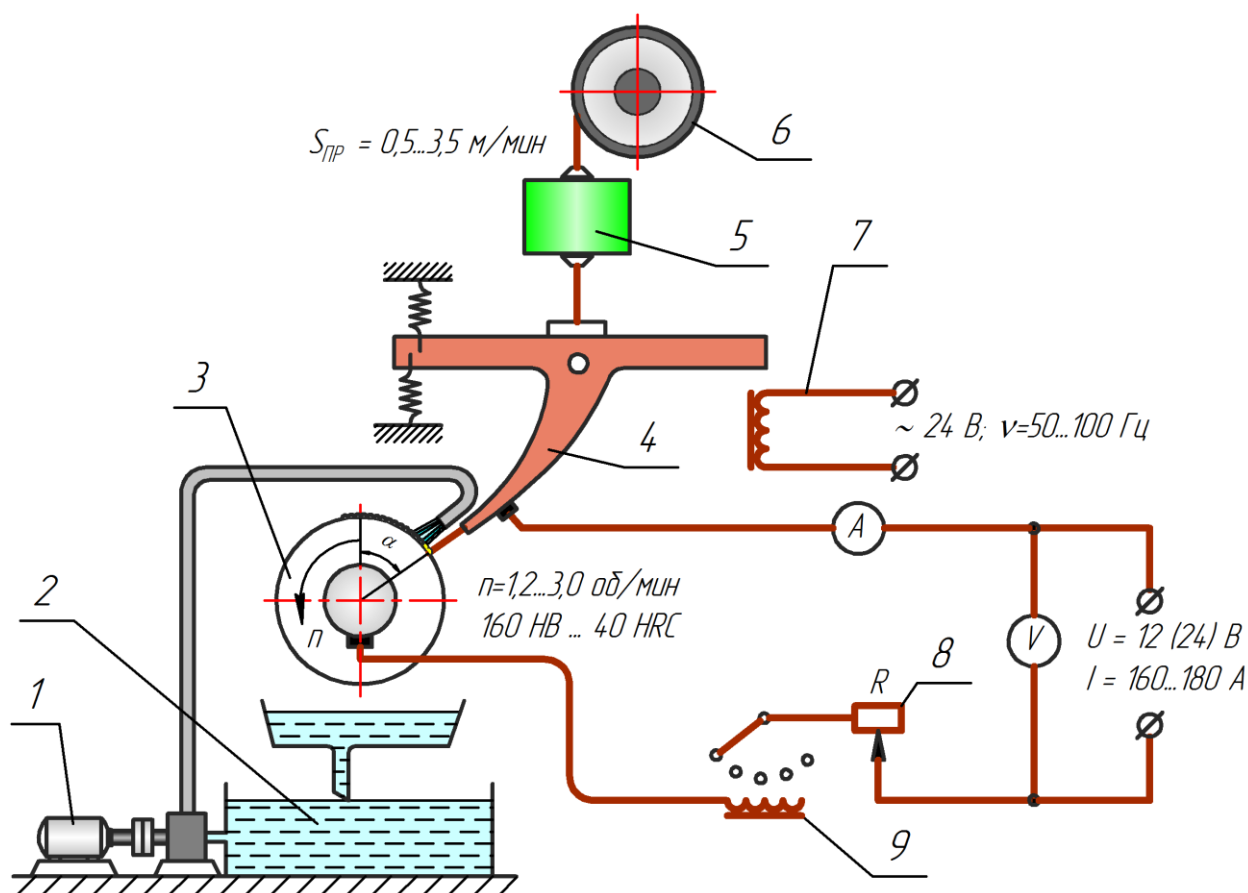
Схема установки для вибродуговой наплавки:
